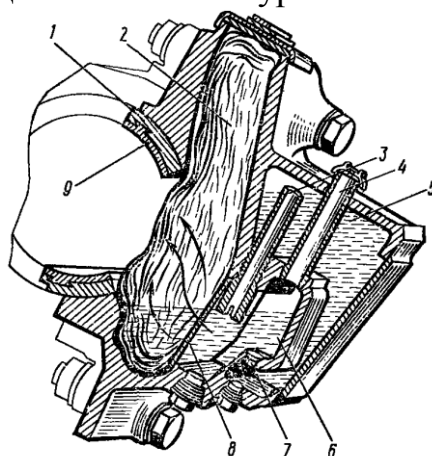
Устройство для смазки моторно-осевого подшипника
